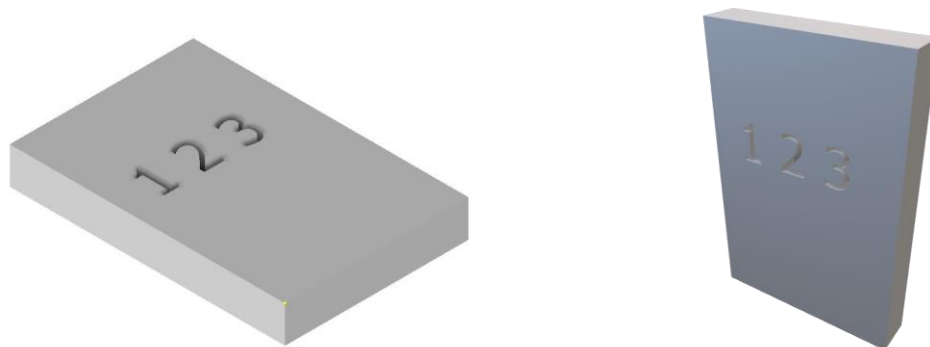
Τρισδιάστατη απεικόνιση αποστολής 33
